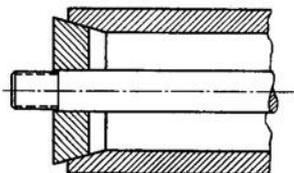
Zentrierung der Werkzeugwellen auf den Arbeitswellen einer Kehlmaschine.
